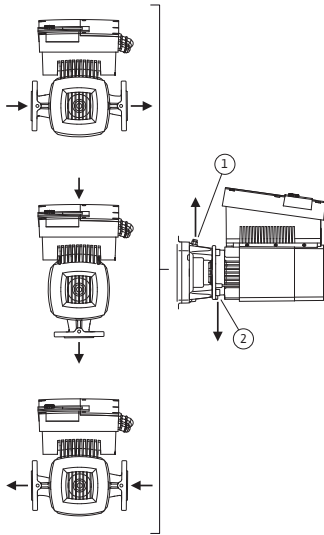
Formas de montaje permitidas con eje del motor en posición horizontal
